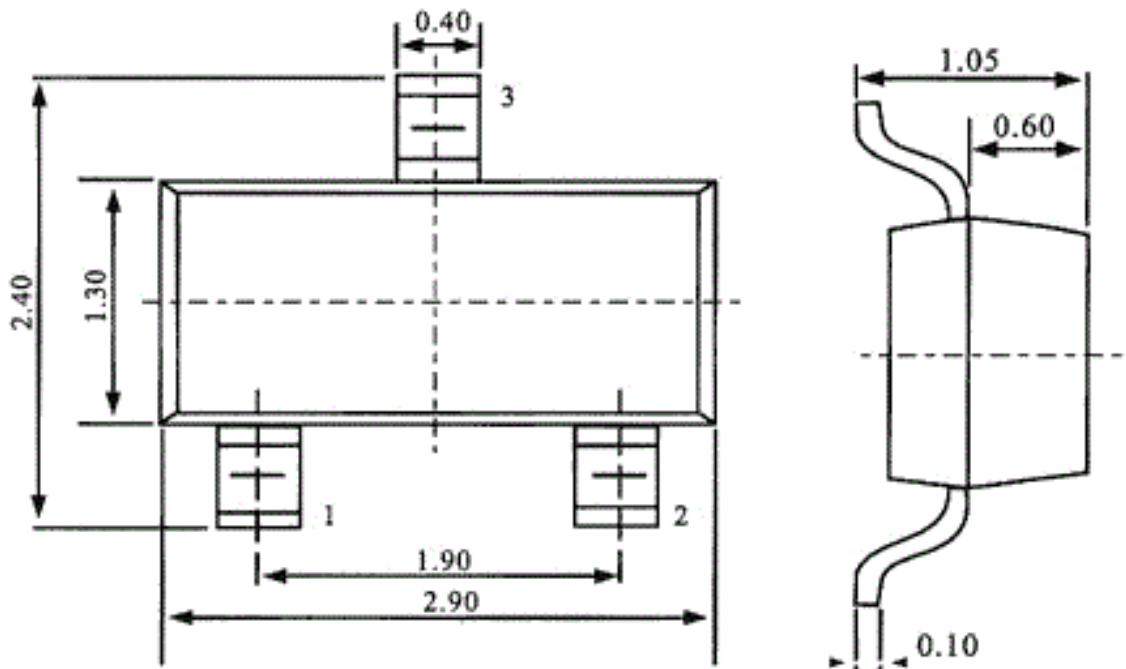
Габаритні розміри стандартного корпусу SOT23
